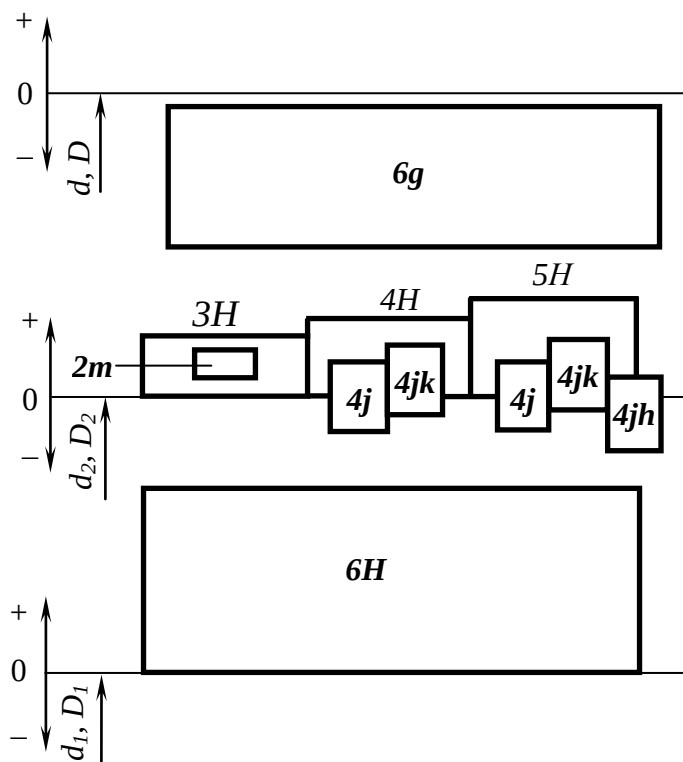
Схемы полей допусков резьбовых соединений с переходными посадками
